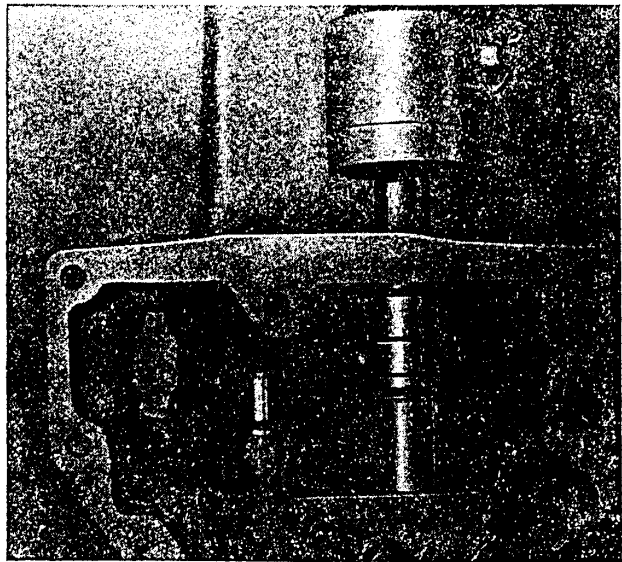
Eindringen des Zwischenradbolzens mit Handhebelpresse
